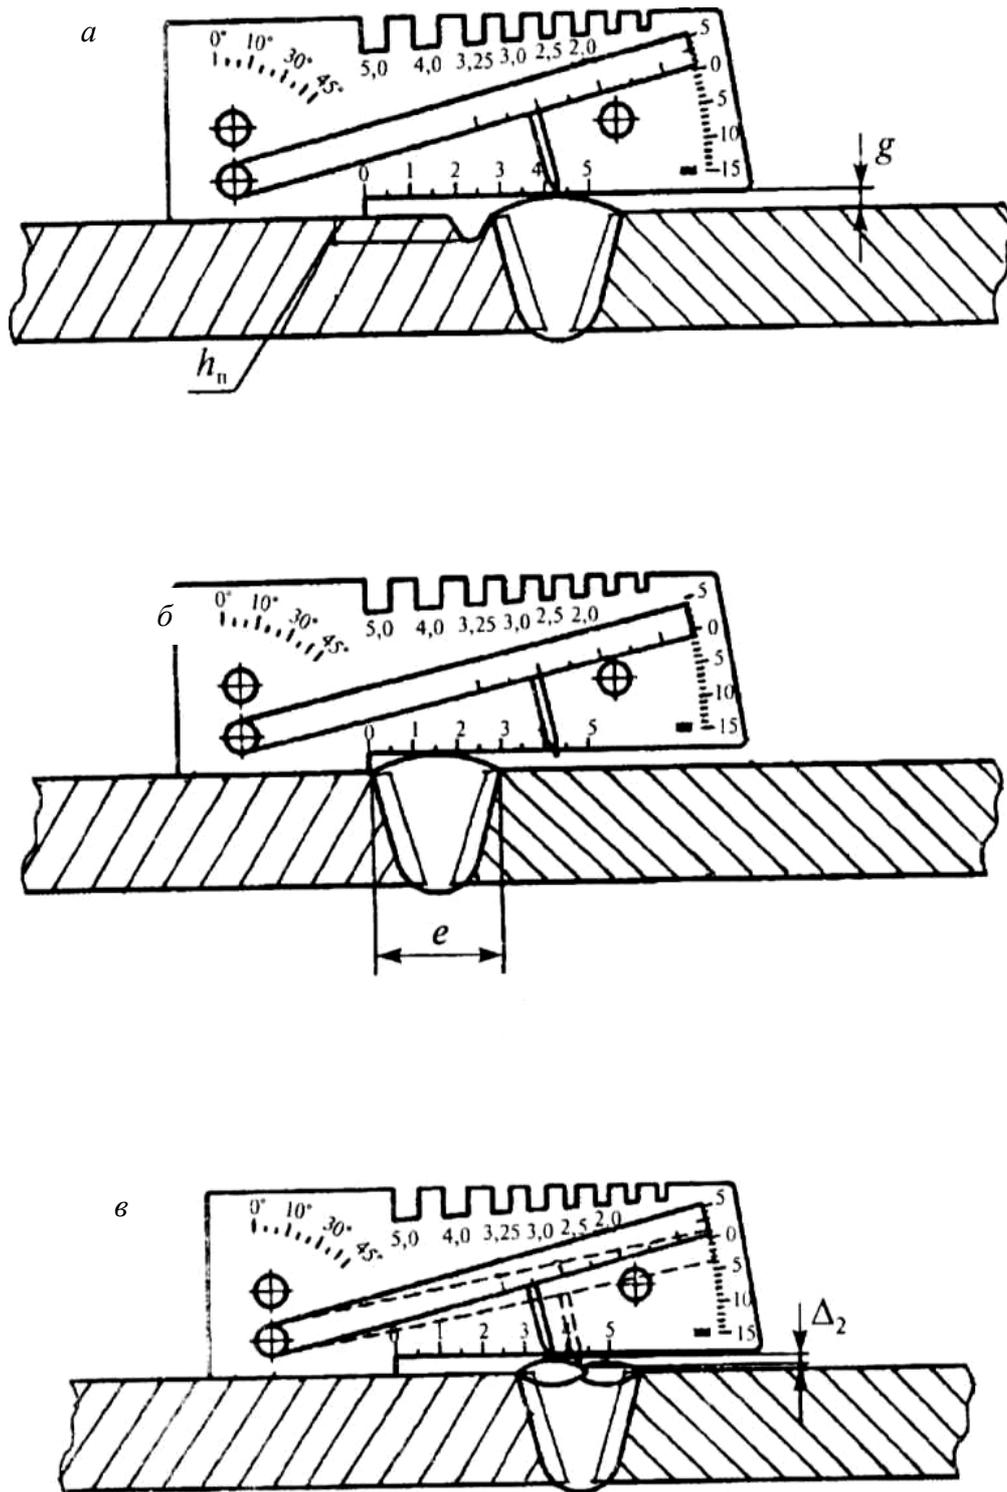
Измерения с помощью шаблона УШС размеров сварного шва:
